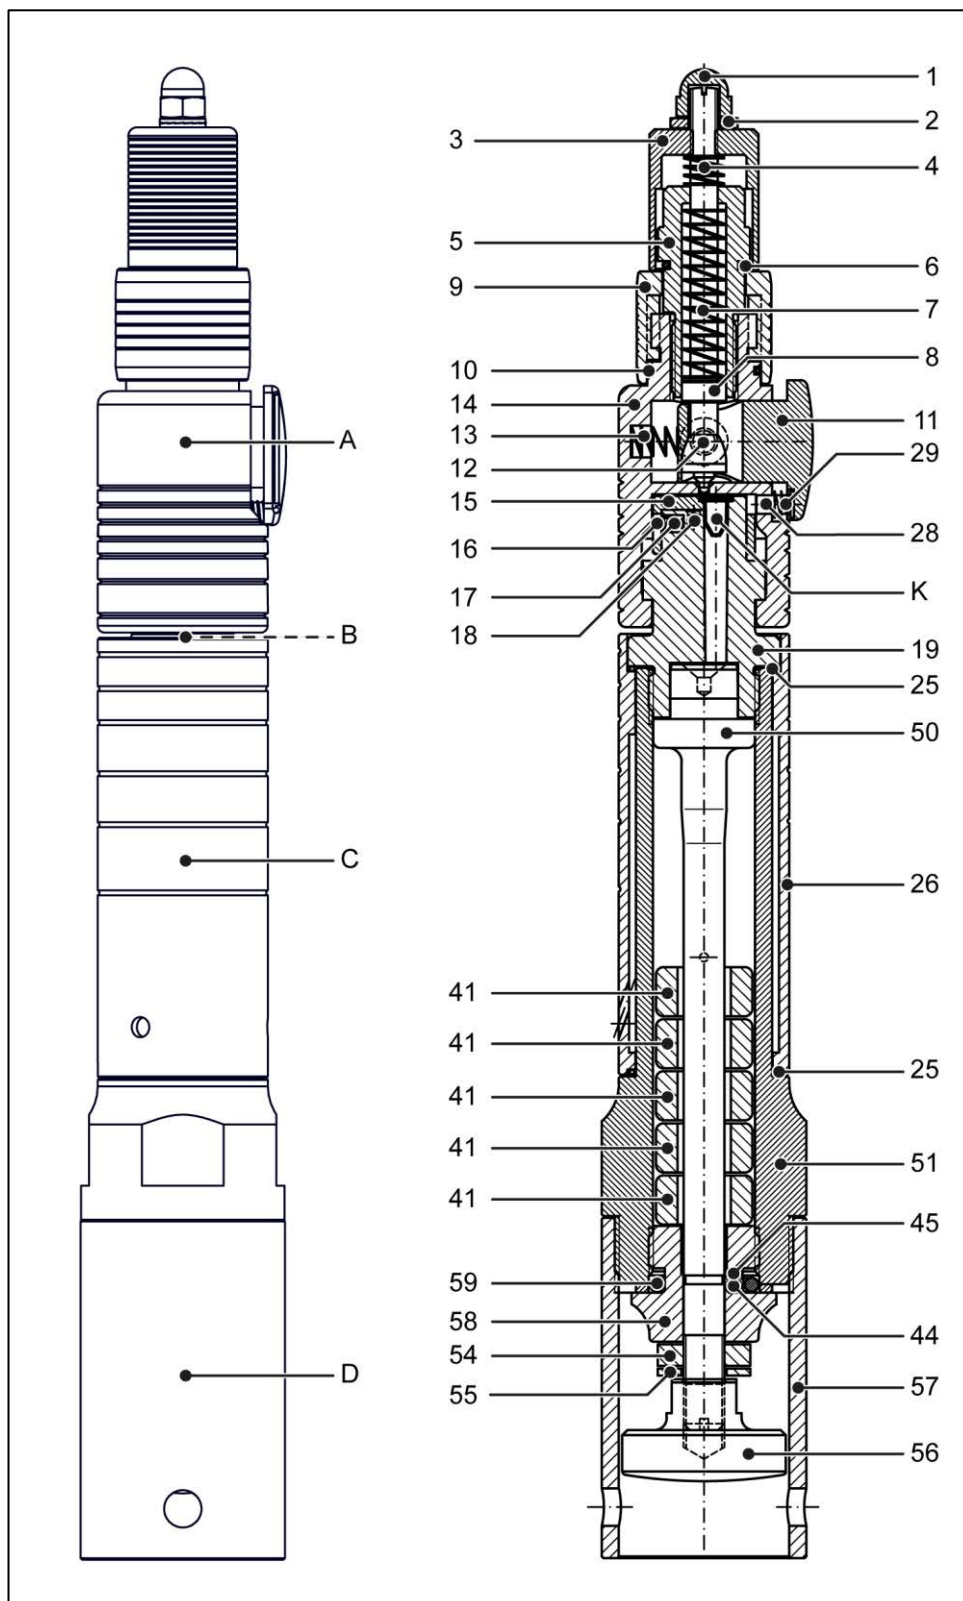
Baugruppen/Bauelemente Typ KC
